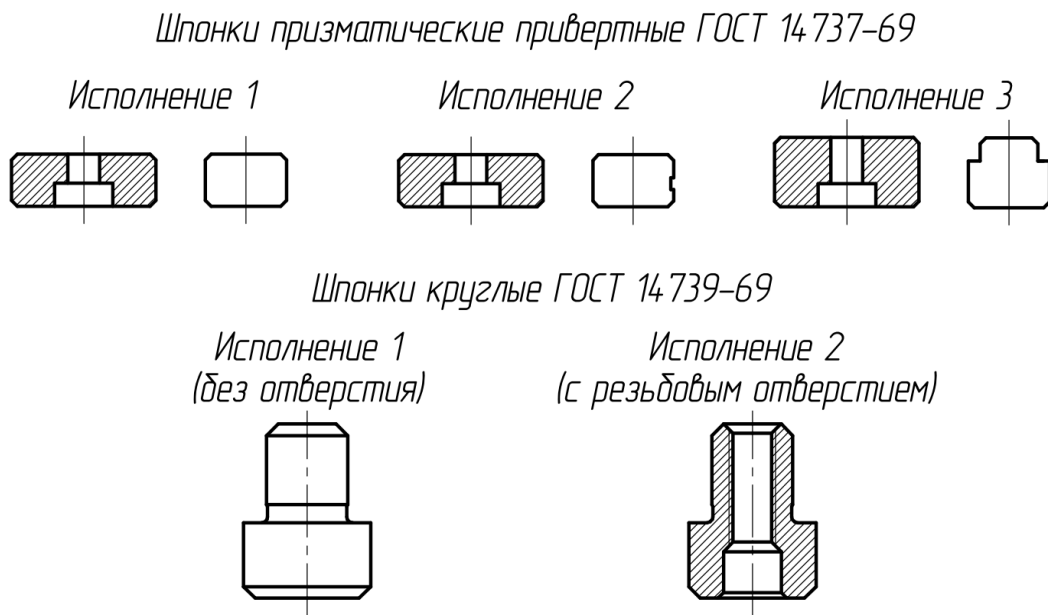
Варианты исполнения шпонок для базирования приспособлений
